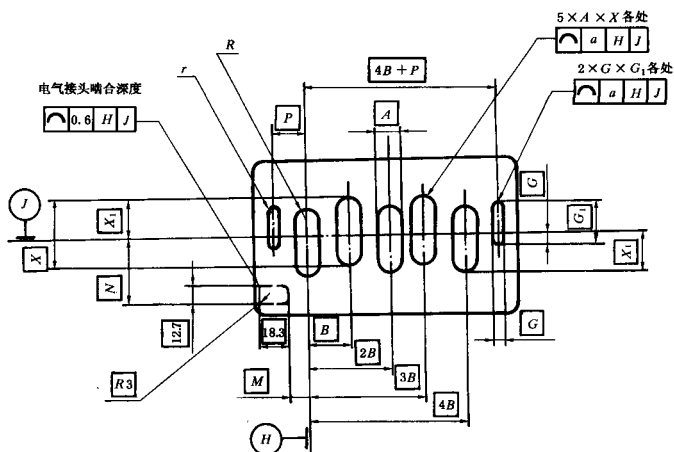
规格4E、5E、6E安装面的外形尺寸和公差
